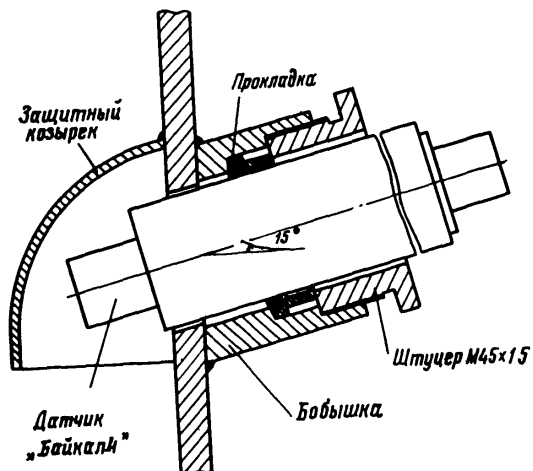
Установка датчика "Байкал-4" в стену камеры
